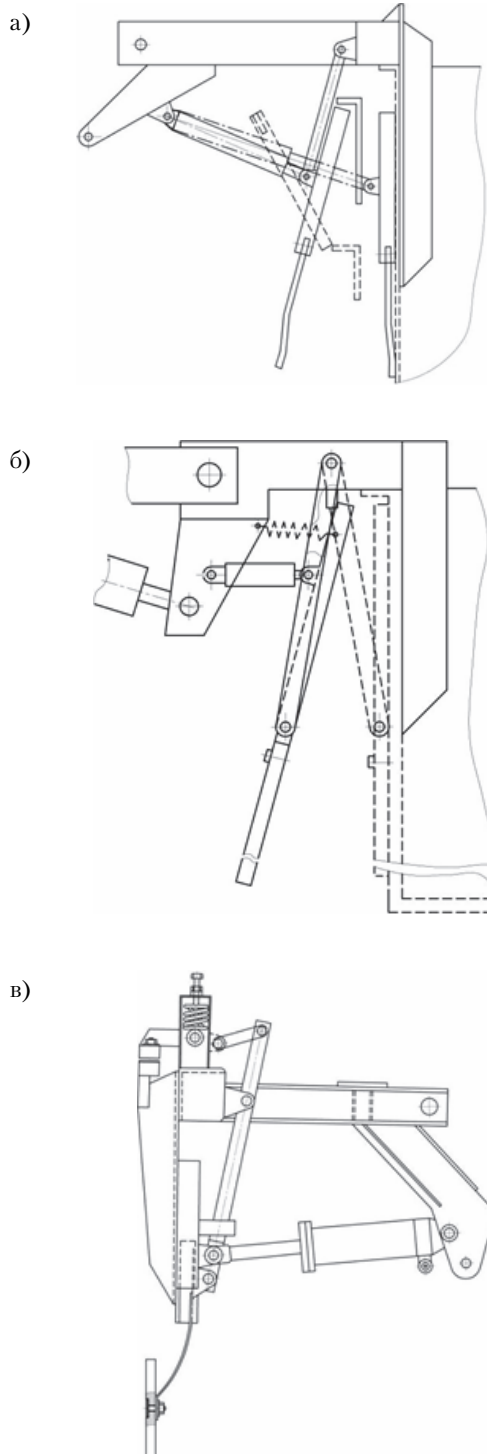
Анализ захватов манипуляторов мусоровозов с боковой загрузкой: а) конструкция захвата мусоровозов серии КО (авторское свидетельство SU1622237); б) подъемно-опрокидывающее устройство с поддерживающим приспособлением для контейнеров (авторское свидетельство SU11266512); в) устройство для разгрузки металлических и пластмассовых контейнеров (патент RU2177901).
